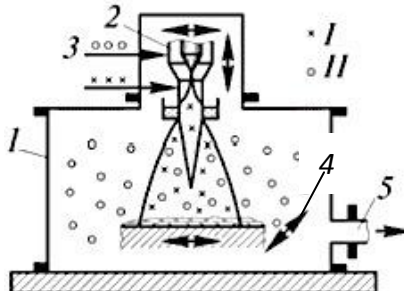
Схема плазменного с общей защитой в камере [16]:
